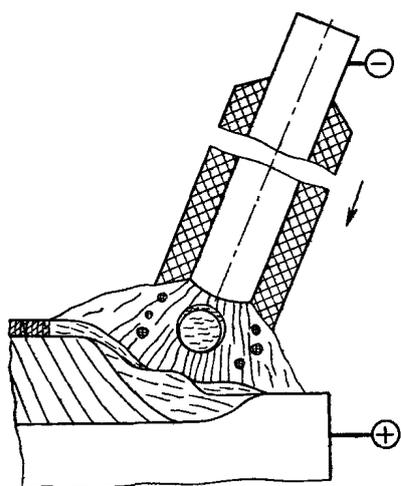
Схема подключения источника сварочного тока при прямой полярности
